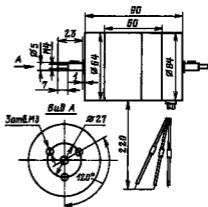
28 Габаритные и установочные размеры двигателя AM-003-2
